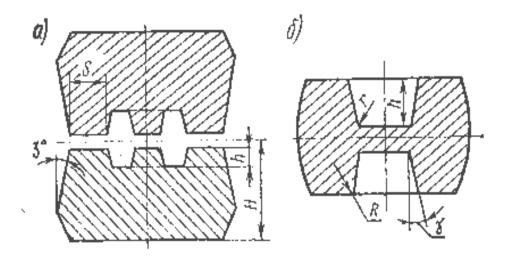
Схемы конструктивных элементов вальцовочных штампов (a) и поковки (б)
